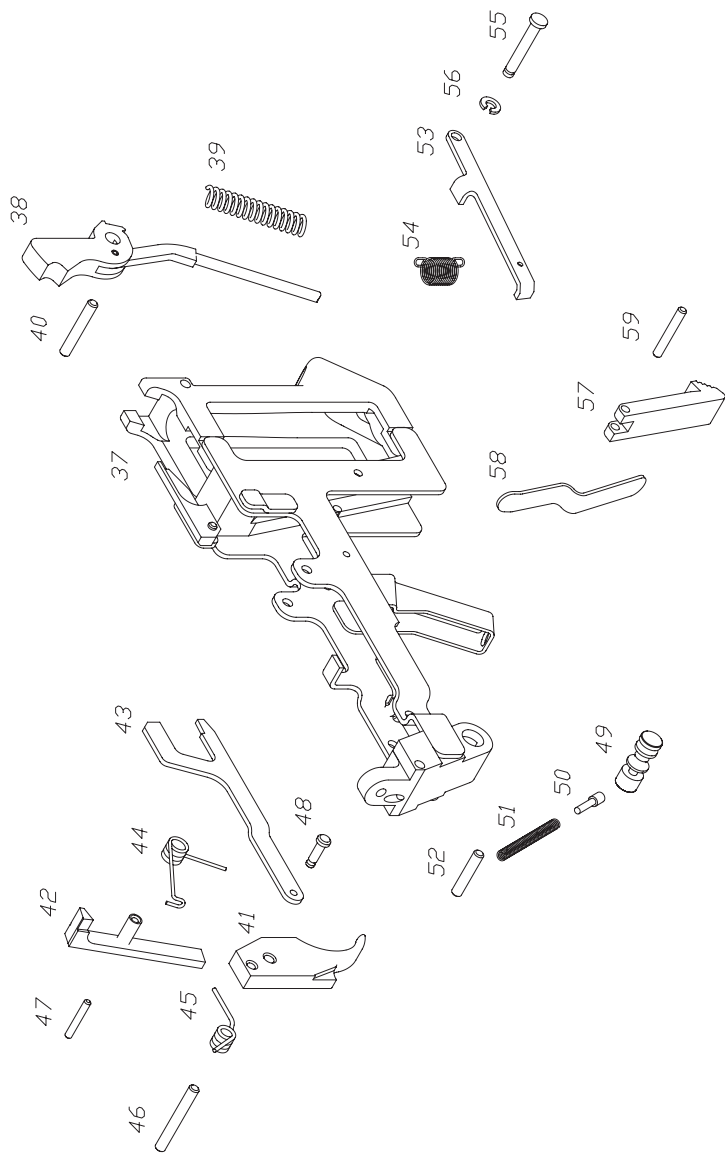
Ударно-спусковой механизм карабина.
